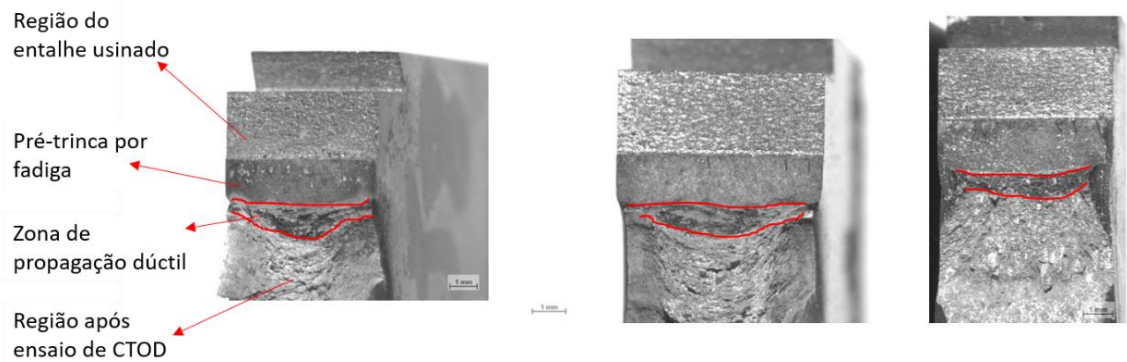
Ensaio CTOD realizado nos corpos de prova retirados da junta soldada HLAW – GMAW
